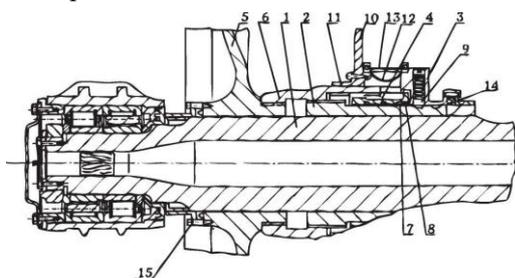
Схема конструкции РКП с жидкой смазкой
